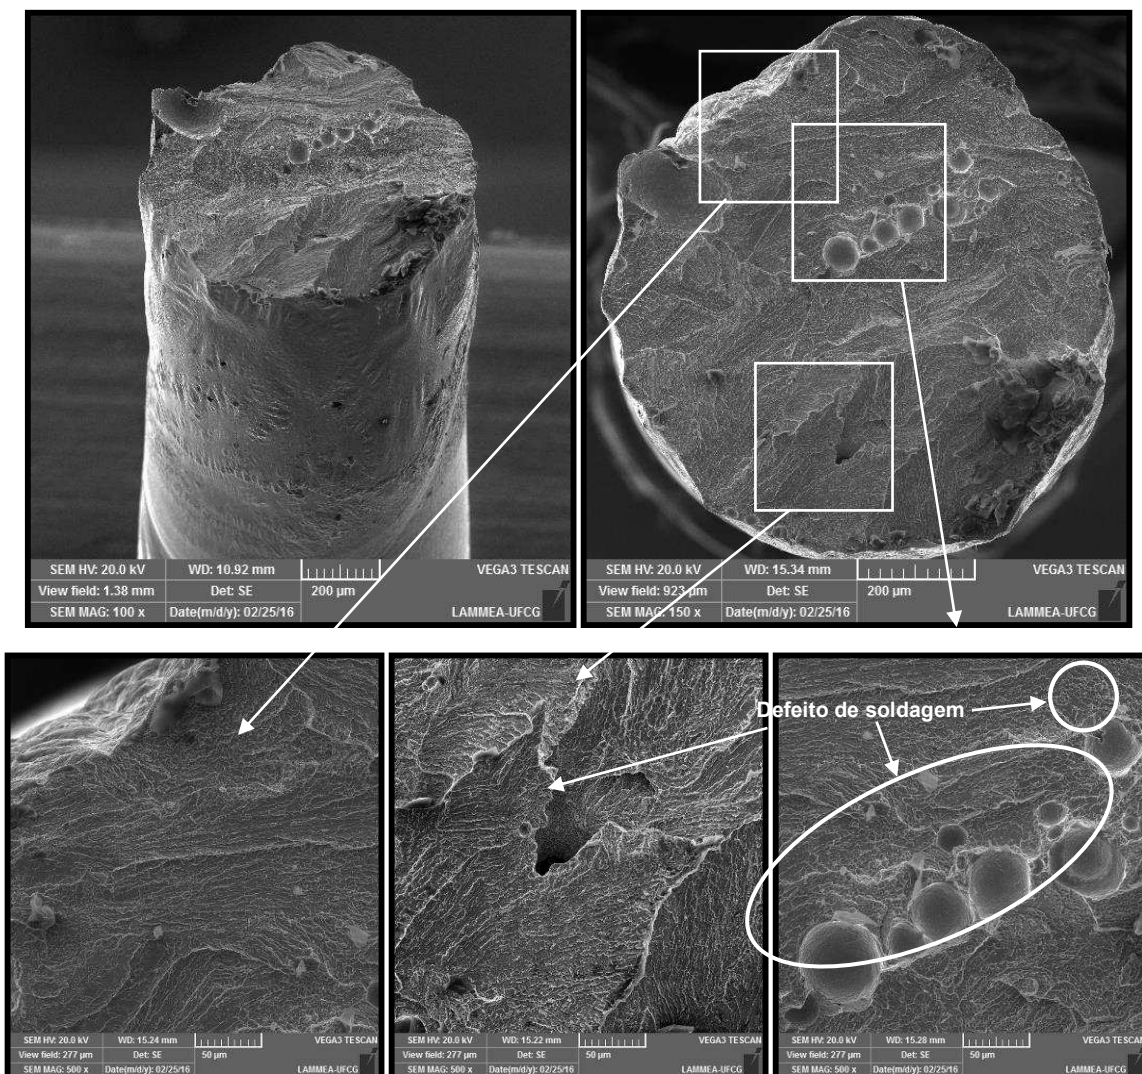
Superfície de fratura do fio superelástico soldado na configuração 8ms/65% testado a 90°C.
